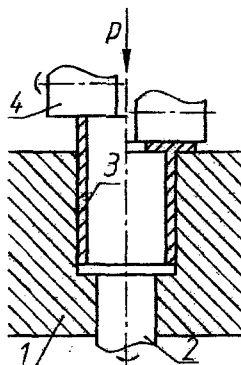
Схема обкатывания роликами без ограничения формы формируемого фланца: 1 – матрица; 2 – вращающийся шпиндель; 3 – втулка-заготовка; 4 – ролик, совершающий обкатку
